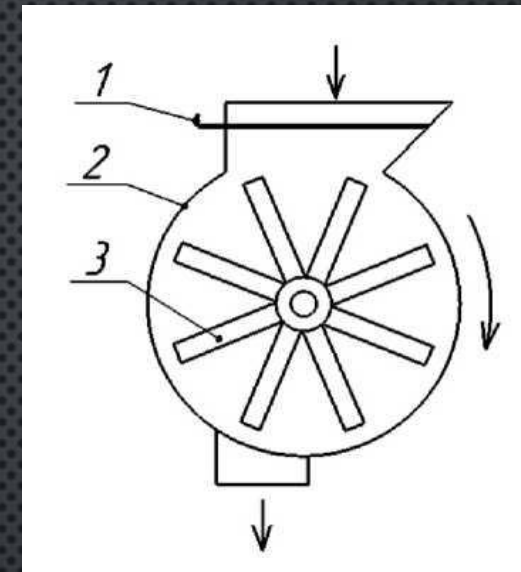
Барабанний дозатор: 1 – заслінка; 2 – корпус; 3 – лопатевий барабан
